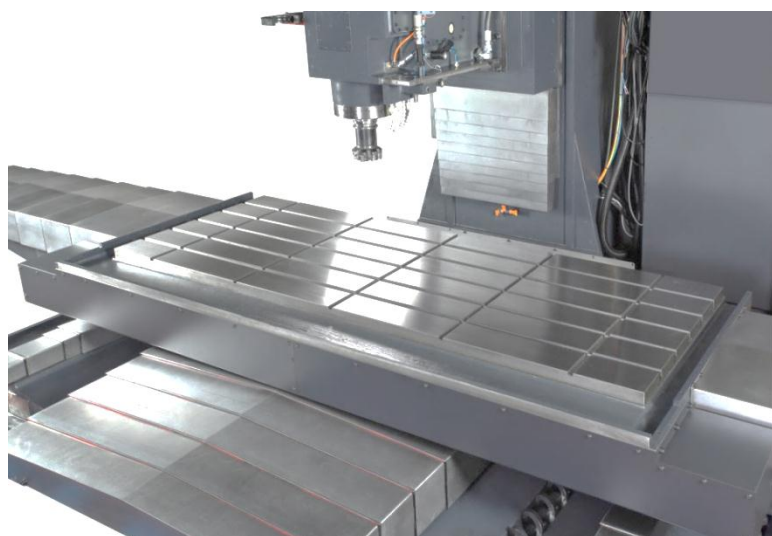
Вертикальный обрабатывающий центр Mynx
